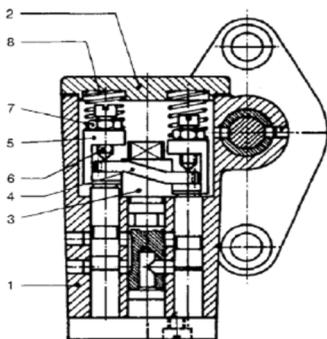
Насос смазки цилиндров компрессора Хатлапа W:
